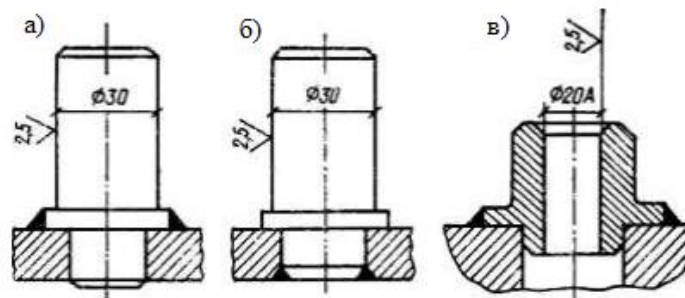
Схема установки приварних чистооброблених фіксаторів
